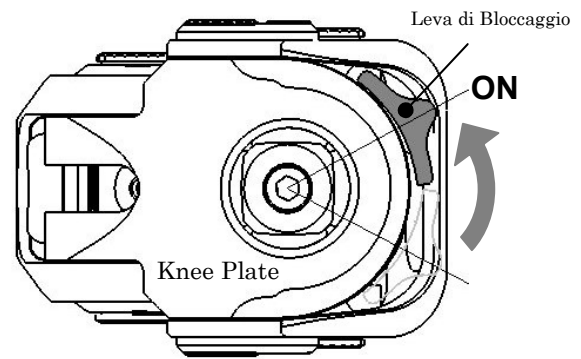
Posizione di bloccaggio della leva (vista dall'alto)
